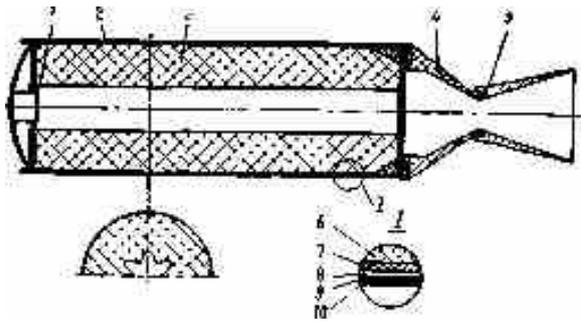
Схема ракетного двигателя на твердом топливе: 1-воспламенитель; 2-корпус двигателя; 3-заряд твердого топлива; 4-сопло; 5-графитовый вкладыш; 6-топливо; 7-бронировка; 8-зазор; 9-теплоизоляция двигателя; 10-стенка корпуса
